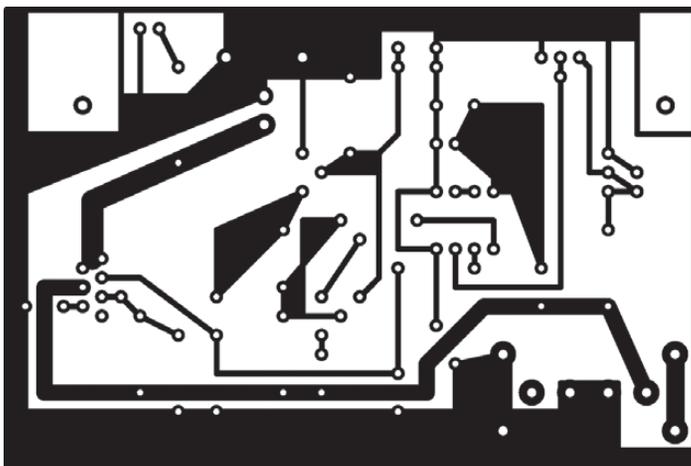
Leitungsführung der Platine für die Schutzschaltung 3; Abmessungen 92 mm × 61 mm, M 1:1
